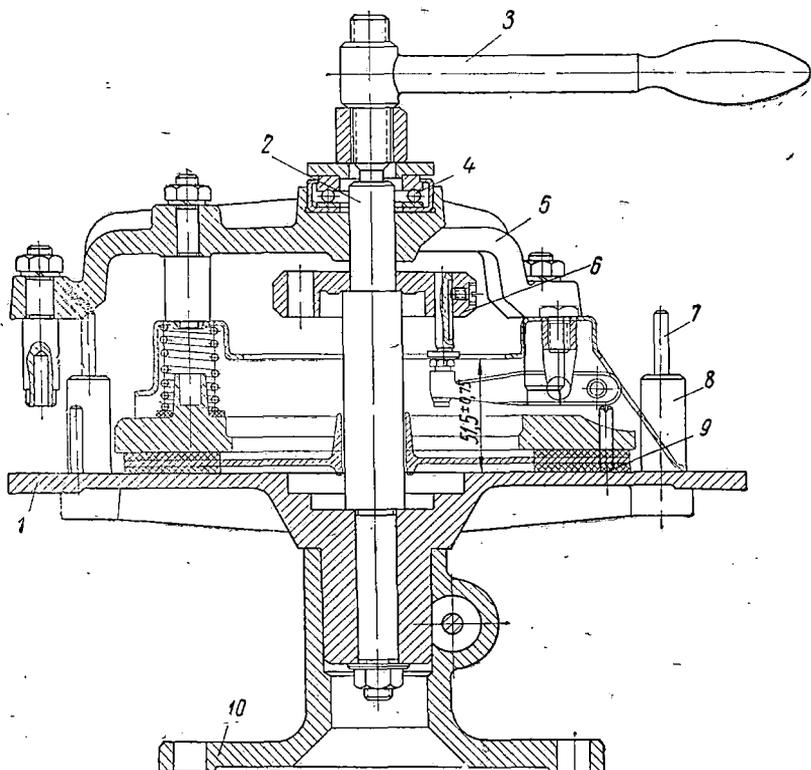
Приспособление для сборки, разборки и регулировки сцепления:
